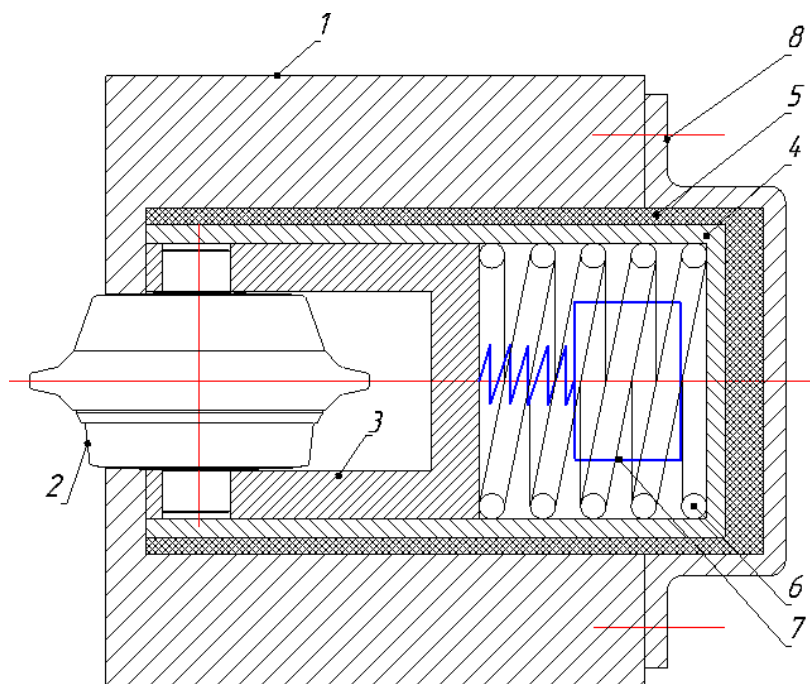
Конструктивная схема виброактивной шарошки:
